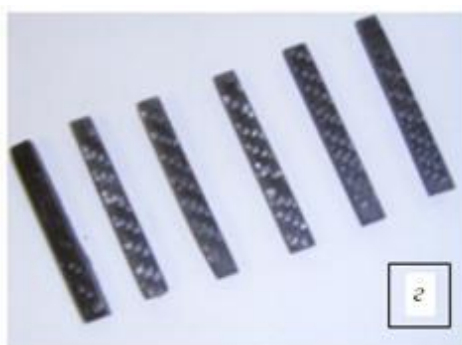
Изготовления образцов гибридных нанокompозитов
